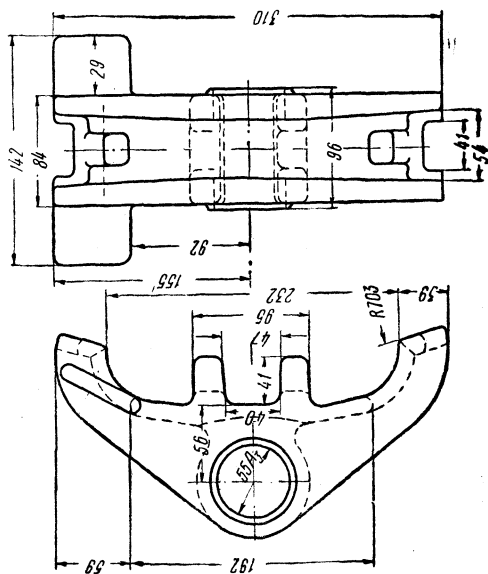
Башмак с посадкой на круглую цапфу, триангеля и чековым креплением колодки электровозов
